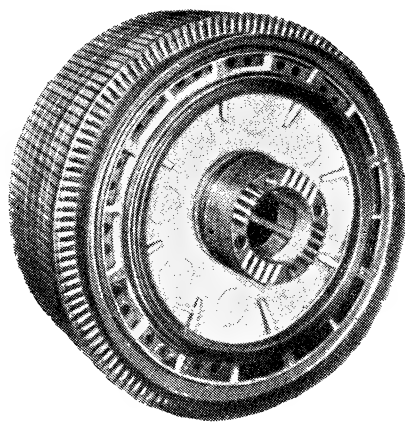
Конструкция двигателя при передаче гибкими пластинами.
